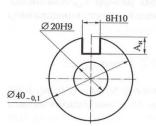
Эскиз обрабатываемой детали к заданию 1.34
